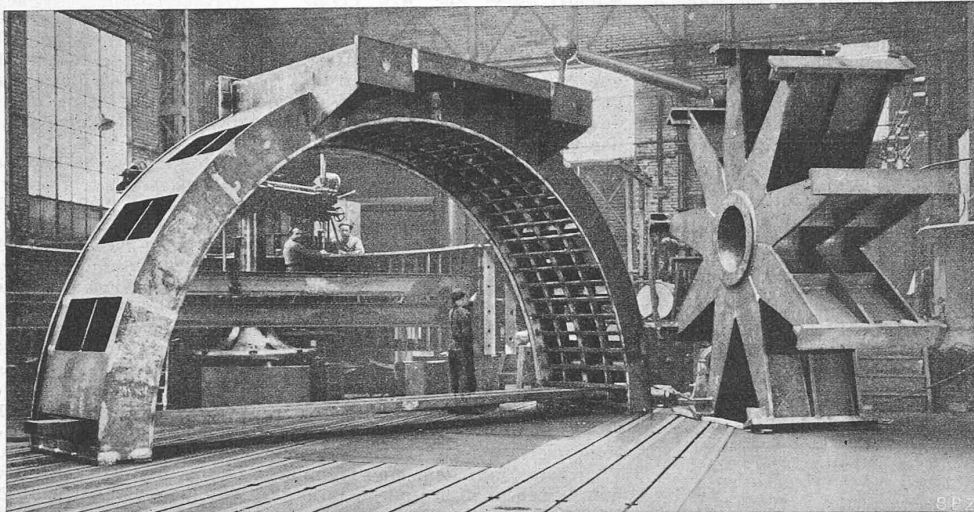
Statorhälfte und Rotorstern in elektrisch geschweisster Ausführung, desgleichen rechts:
